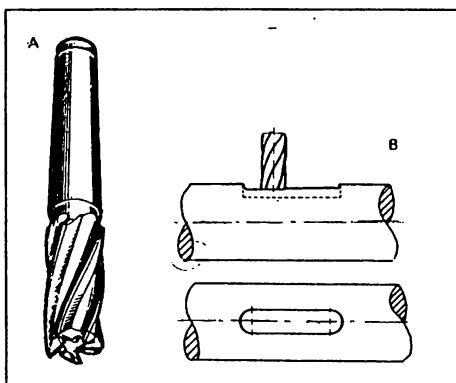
Fresa frontal para hacer chaveteros; A, fresa; B, forma de trabajo.
